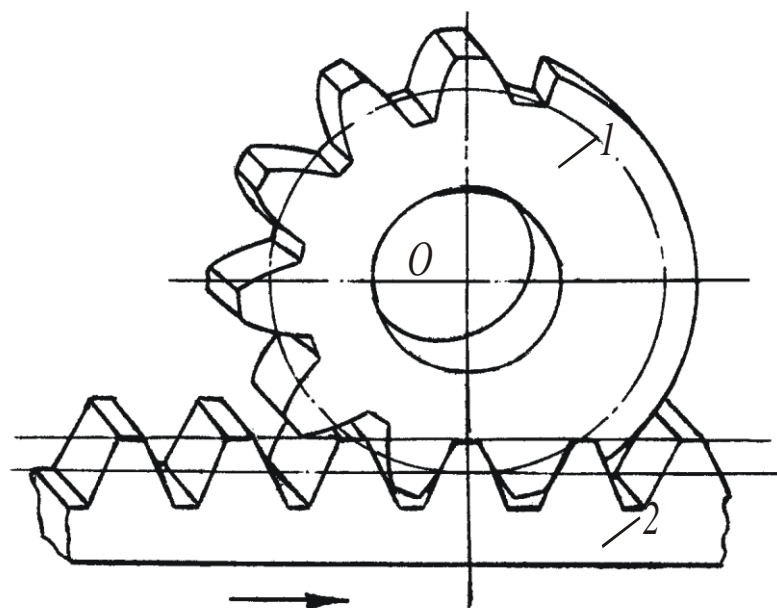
Зубчаста пара "евольвентне колесо-рейка"
